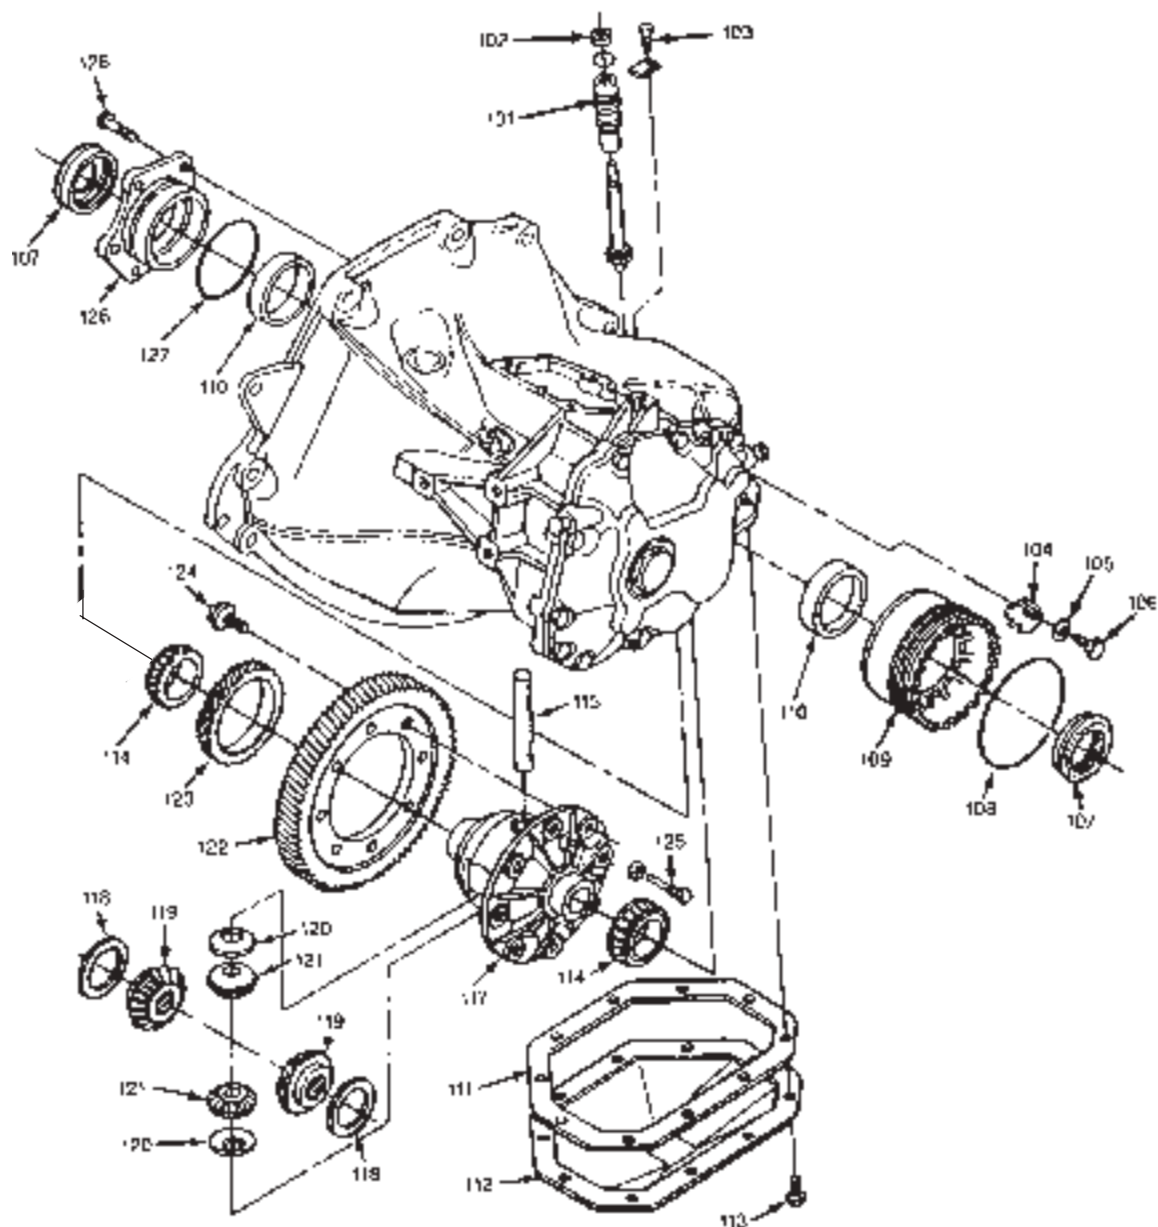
Vedere explodată – pinioane și carcasă F16 (cinci viteze)
